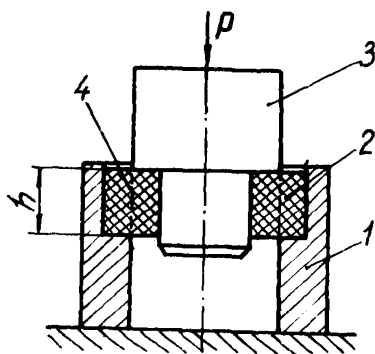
Схема испытания раструбного сварного соединения на сдвиг:
